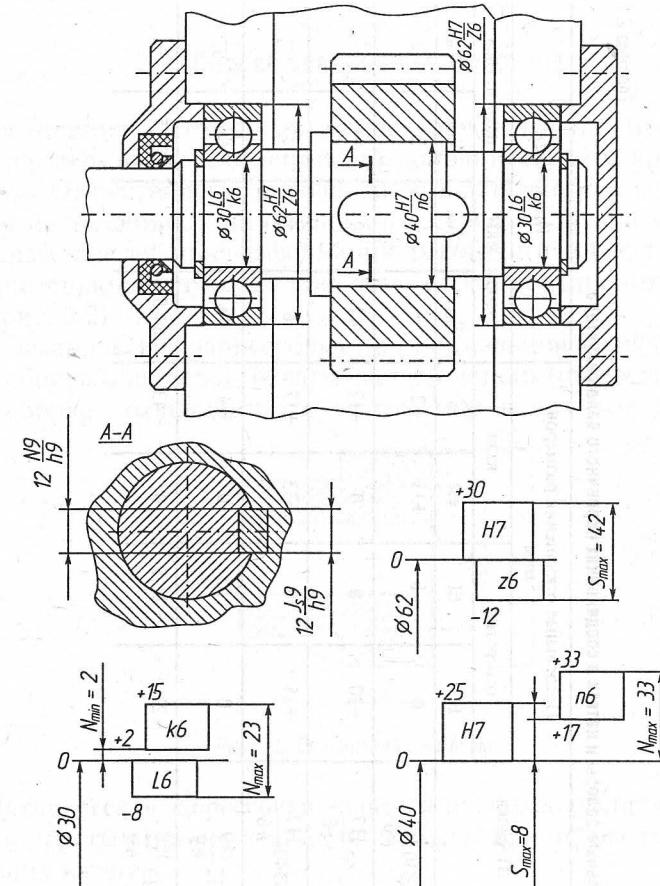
Первичный вал редуктора в сборе и схемы полей допусков соединений
